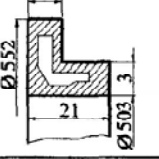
Кольцевые заготовки, изготовленные прокаткой, гибкой и сваркой
